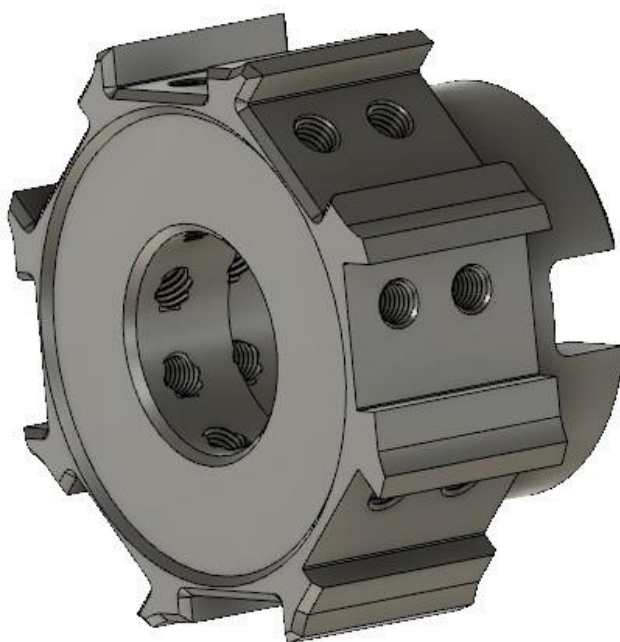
3D модель корпус розвертки збірної,
